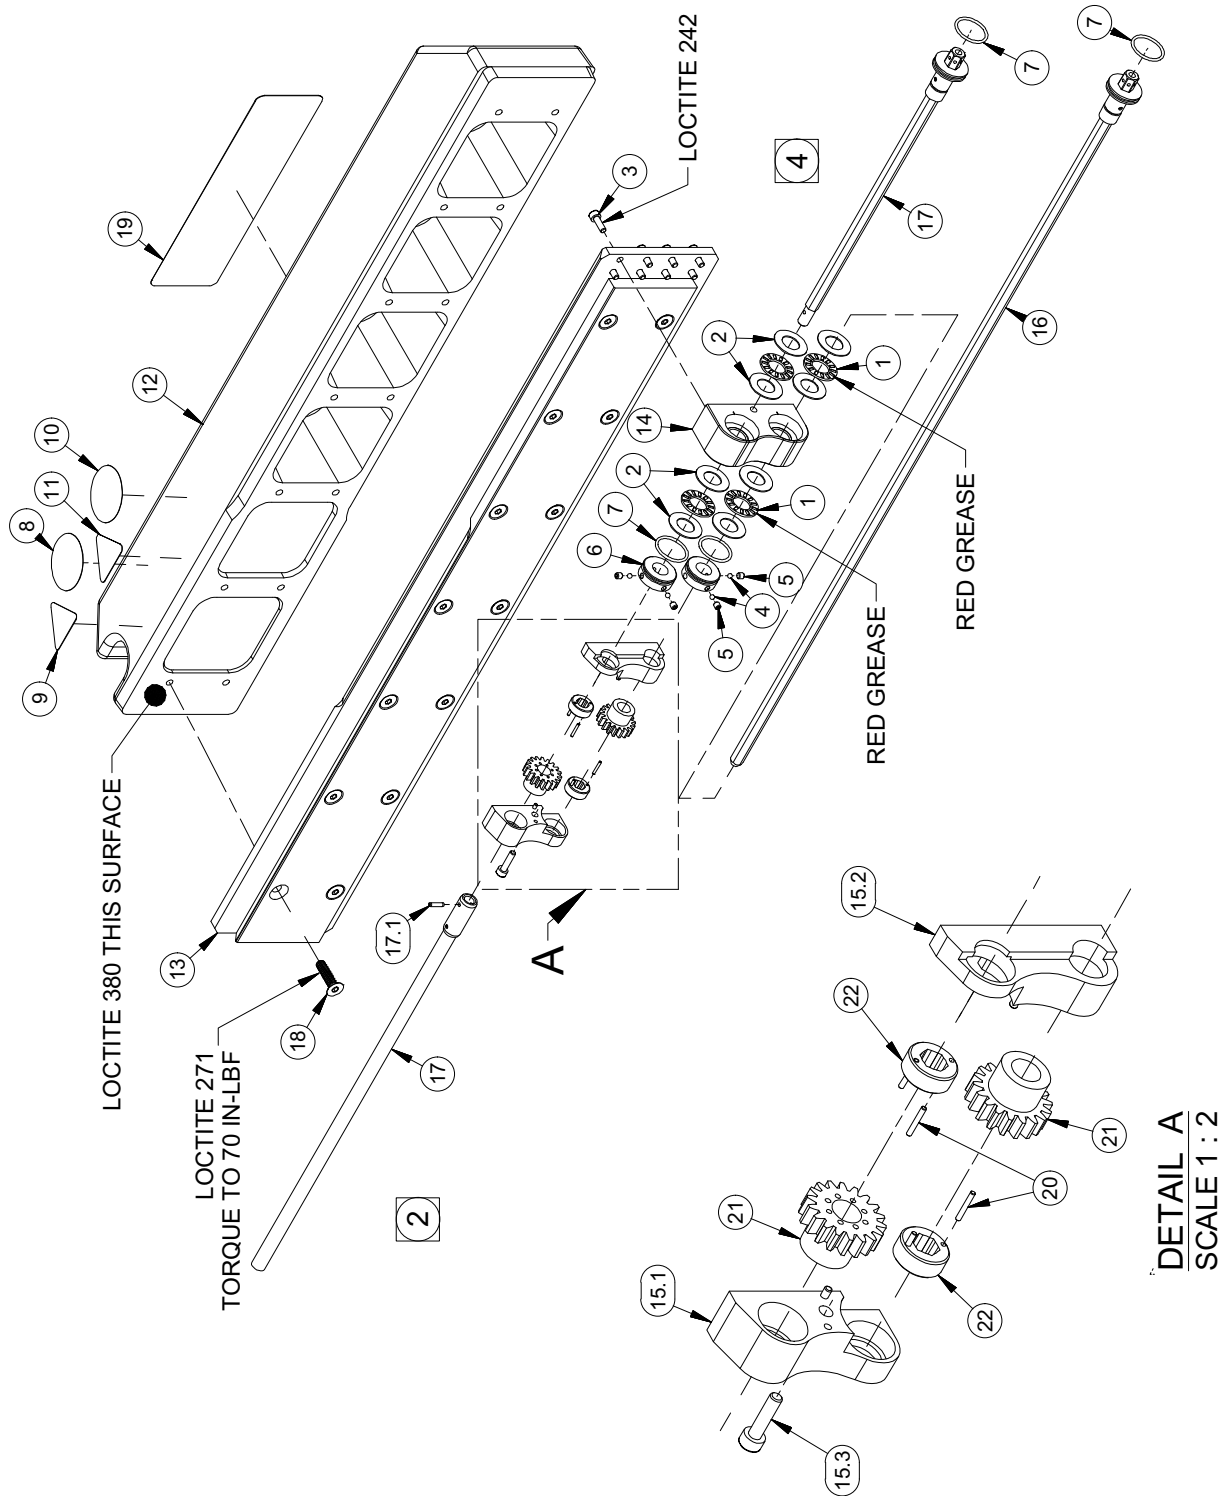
ENSEMBLE BRAS D'USINAGE (P/N 90337 RÉVISION E)
